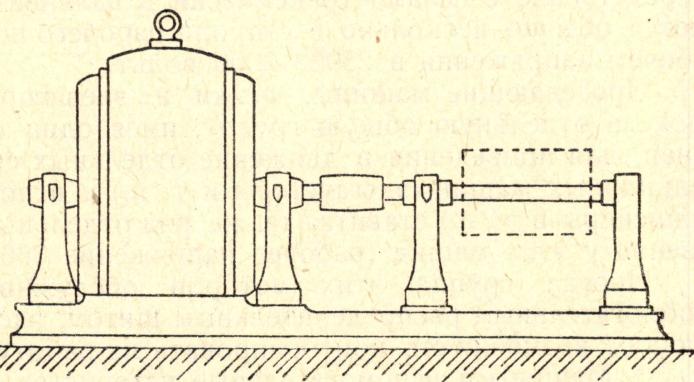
Трехфазный двигатель с дополнительной боковой стойкой.
